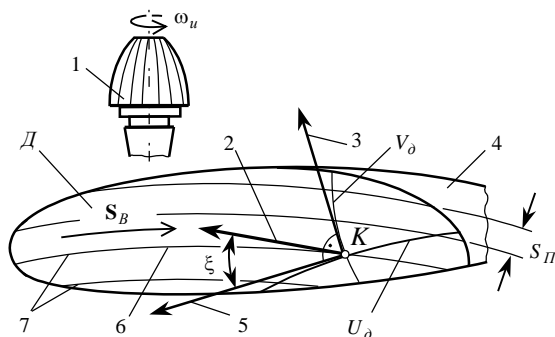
Схема способа обработки сложных поверхностей детали (а.с. №1255304).
